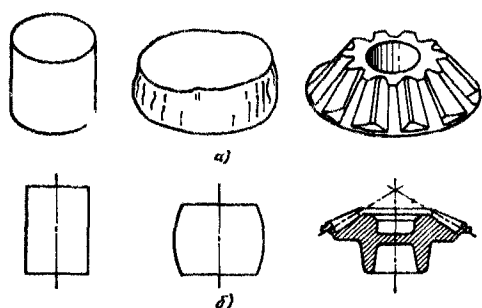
Схемы горячей штамповки заготовок конических колес с прямыми зубьями:
